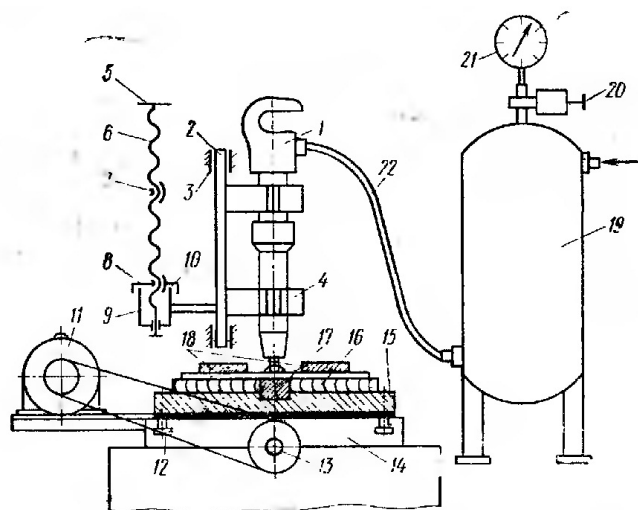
Основные узлы вибромолотка: ударное устройство 1; приспособление для перевода ударного устройства из нерабочего положения в рабочее (подвижная 2 и неподвижная 3, направляющие, ходовой винт 6, неподвижная 7 и подвижная 8 опоры, зажимы 4, рукоятка 5, приспособление для поджима ударного устройства к обрабатываемому материалу (пружина 9 и накидная гайка 10), устройство для крепления обрабатываемого материала и перемещения его в горизонтальном направлении (двигатель постоянного тока 11, ходовой винт 13, ременная передача 12, стол 14, плита 15, наковальня 17, шумо-вибропрокладки 16, прижимы 18, система питания регулировки и контроля давления сжатого воздуха (ресивер 19, вентиль 20, манометр 21, шланги 22)
